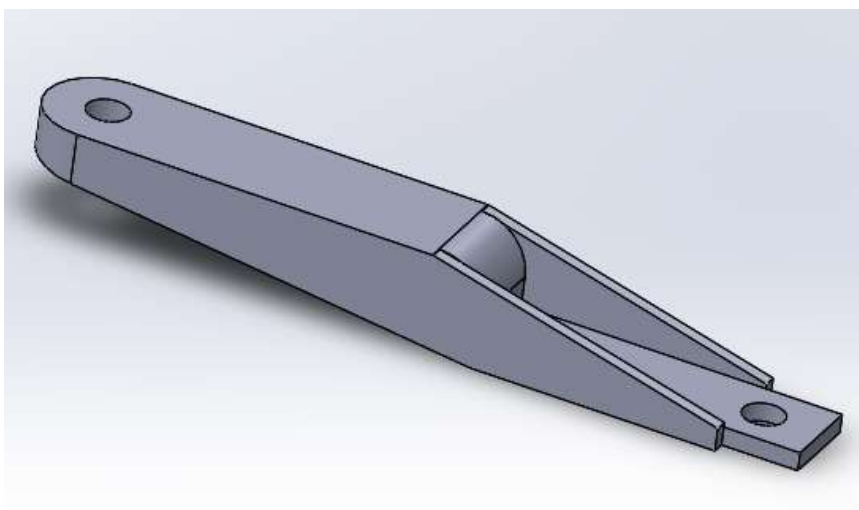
Unión viga lateral-cabezal fijo vista detallada.
